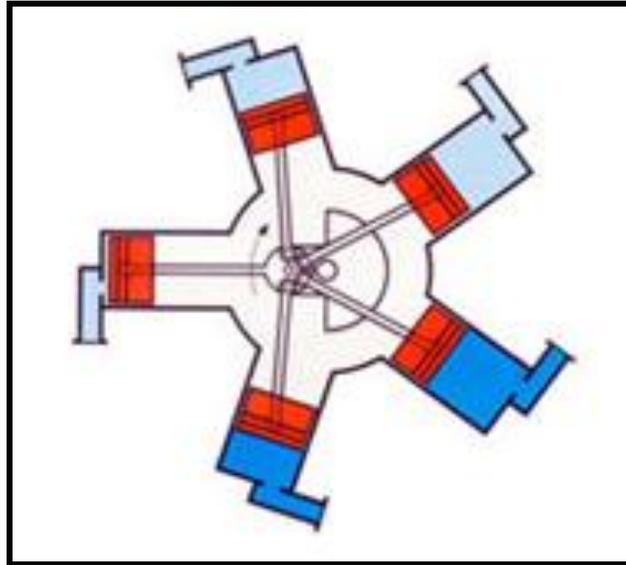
Dibujo representativo de un motor de embolo radial
